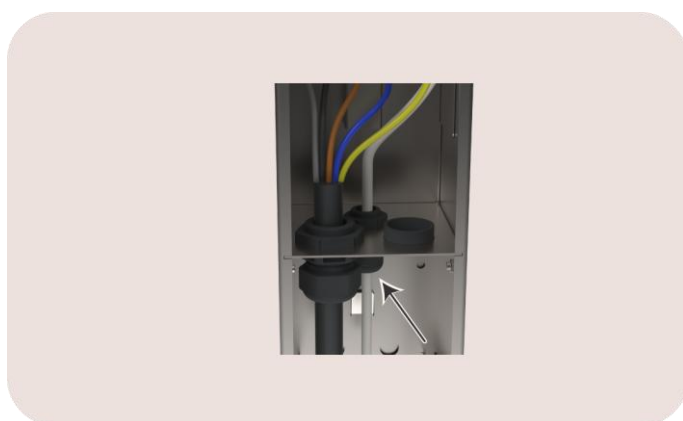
Ansicht der Löcher für die Kabeleinführung
